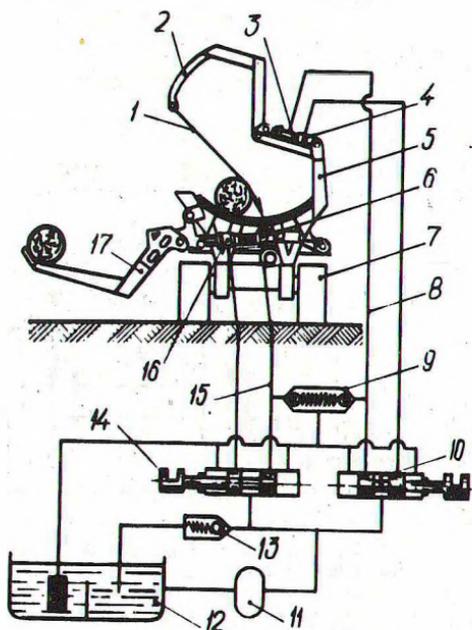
Вид валочно-пакетирующей машины с устройством пакетирования: 1 — трос; 2 — обвязочный рычаг; 3, 4, 16 — гидроцилиндры; 5 — коник; 6 — штоковая полость; 7 — машина; 8, 15 — магистрали; 9 — предохранительный клапан; 10, 14 — золотники; 11 — насос; 12 — масляный бак; 13 — предохранительный клапан; 17 — погрузочный рычаг.
